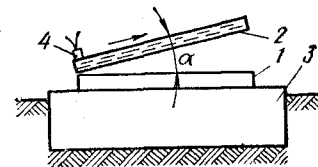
Принципиальная схема сварки взрывом биметаллической заготовки
